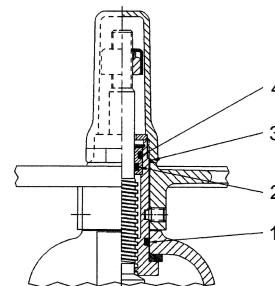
O-ring per valvola di 2,50 – 4,00" (DN 65 – 100)
